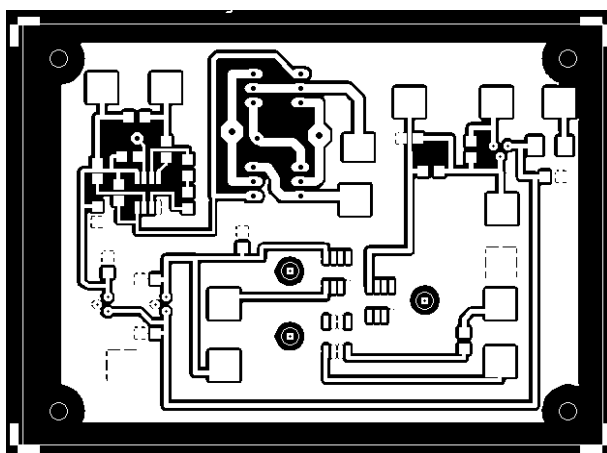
Nosná deska přípravku s DC/DC měničem (192 mm x 163 mm)
